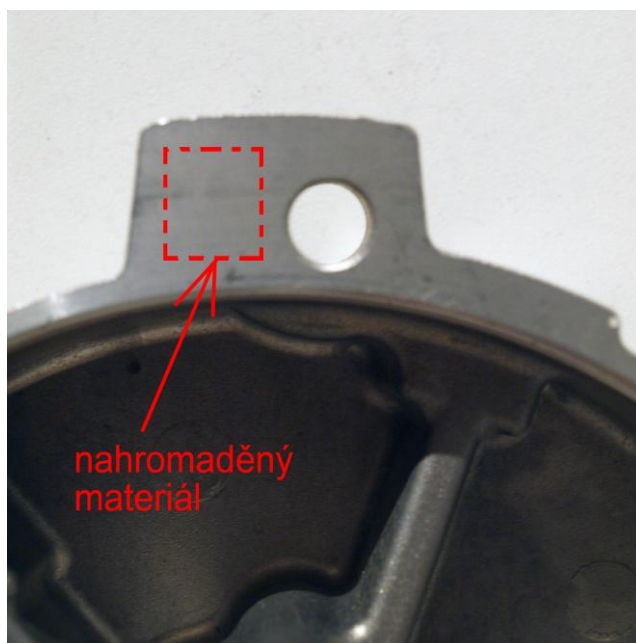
Velká tloušťka materiálu a odlehčení [5]
